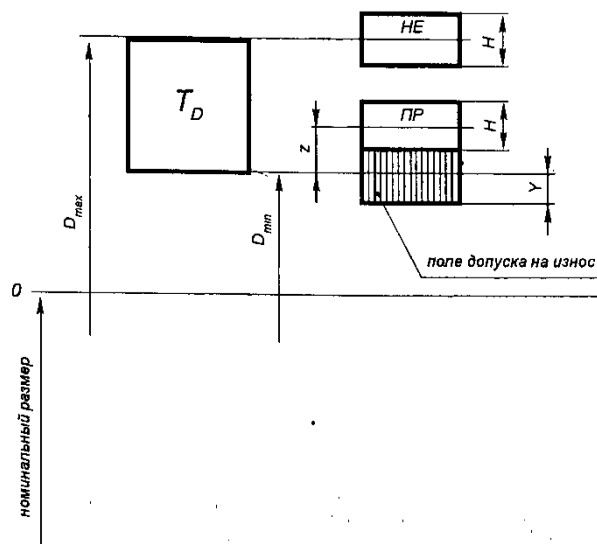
Схема расположения полей допусков калибров для контроля отверстий изготовленных по квалитетам 6, 7 и 8 при номинальных размерах до 180 мм (для размеров отверстий изготовленных по квалитетам от 9 до 17, $Y = 0$)
